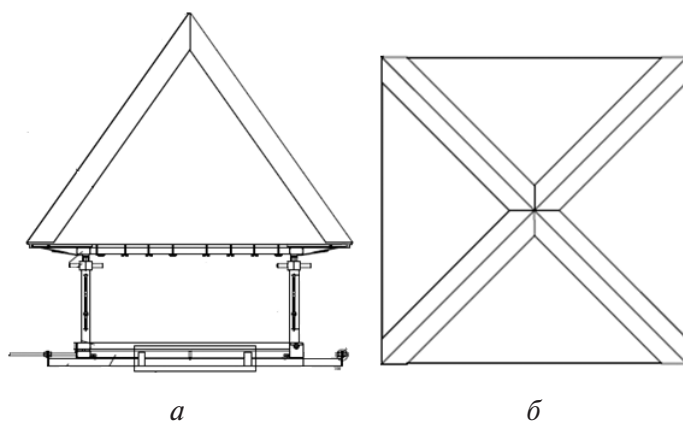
Эскиз УО: а) — вид сбоку; б) — вид сверху
